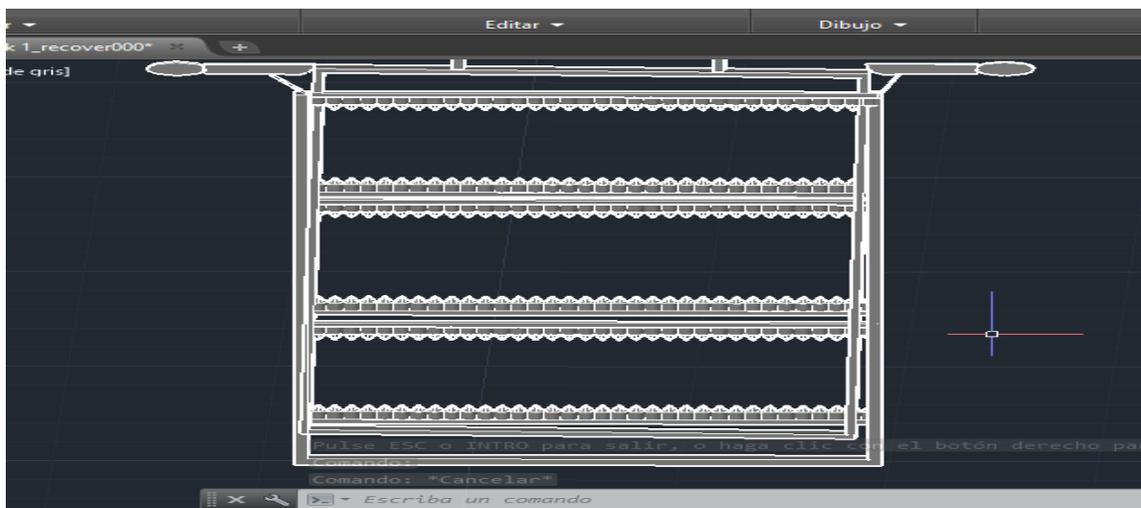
La siguiente imagen muestra el rack para las piezas rectas terminado.
